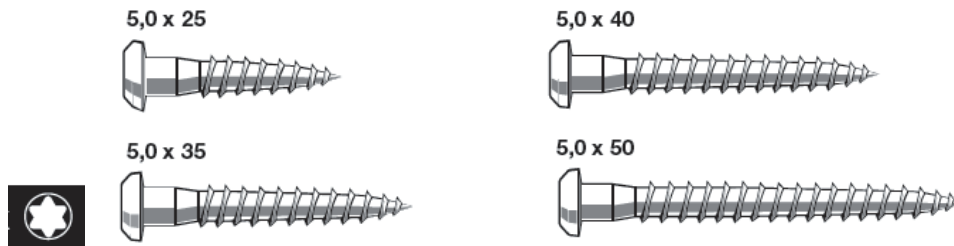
Dimensiones de los Tornillos para conectores cabeza Torx.
